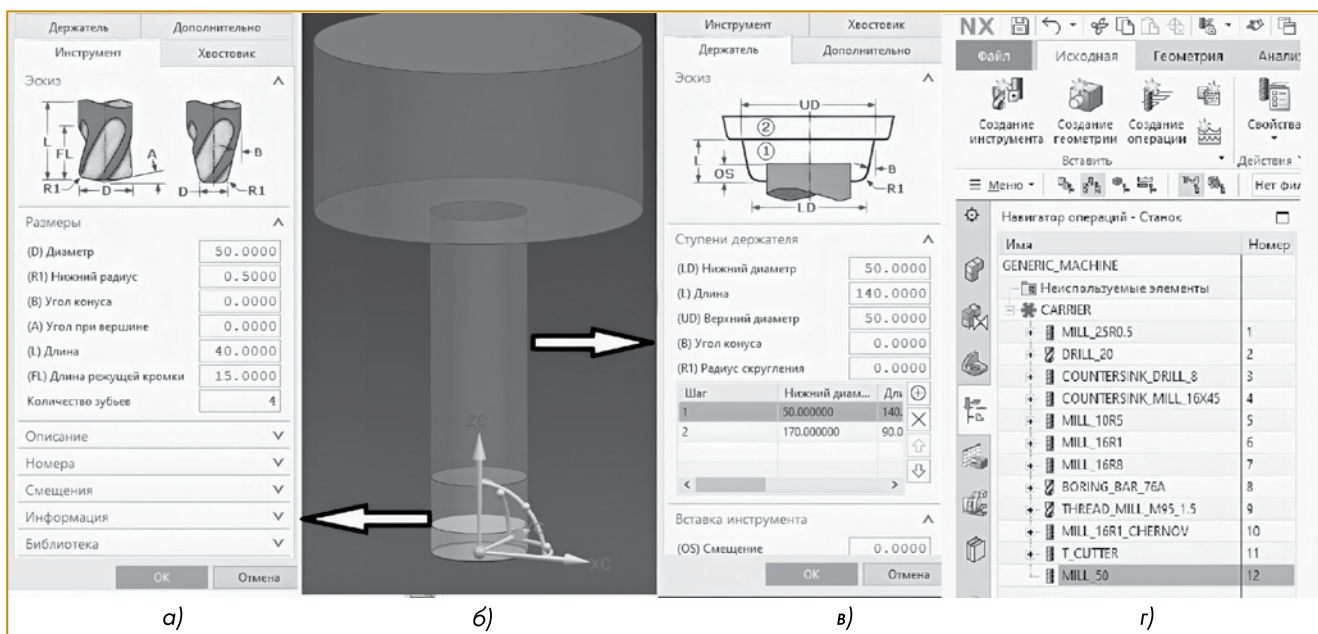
Создание корпусной фрезы SANDVIK R220.69-0050-12-7A в NX CAM:
